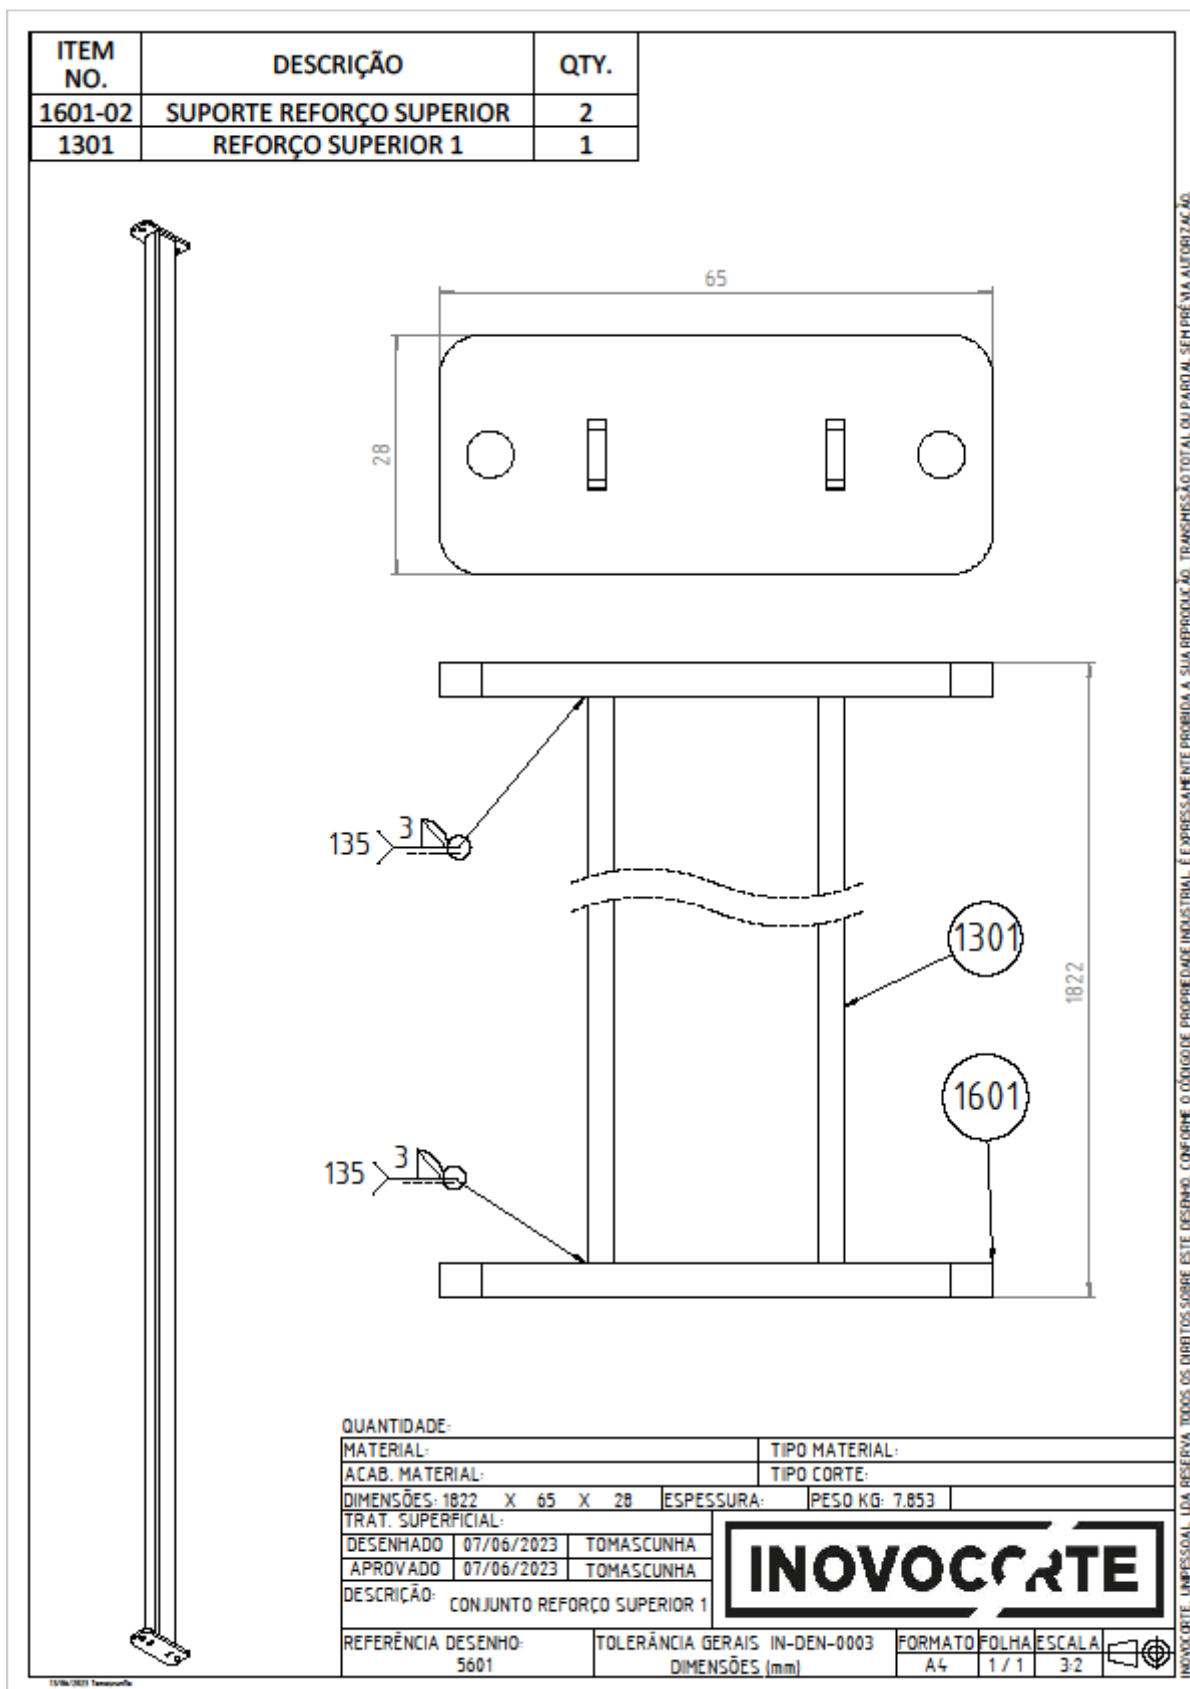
Desenho técnico do conjunto reforço superior 1 (5601).
